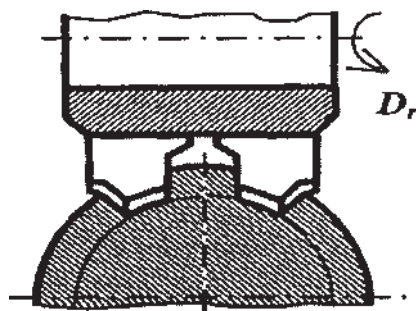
Схема фрезерования шлицевой поверхности дисковой фрезой с одновременной обработкой двух впадин между шлицами
